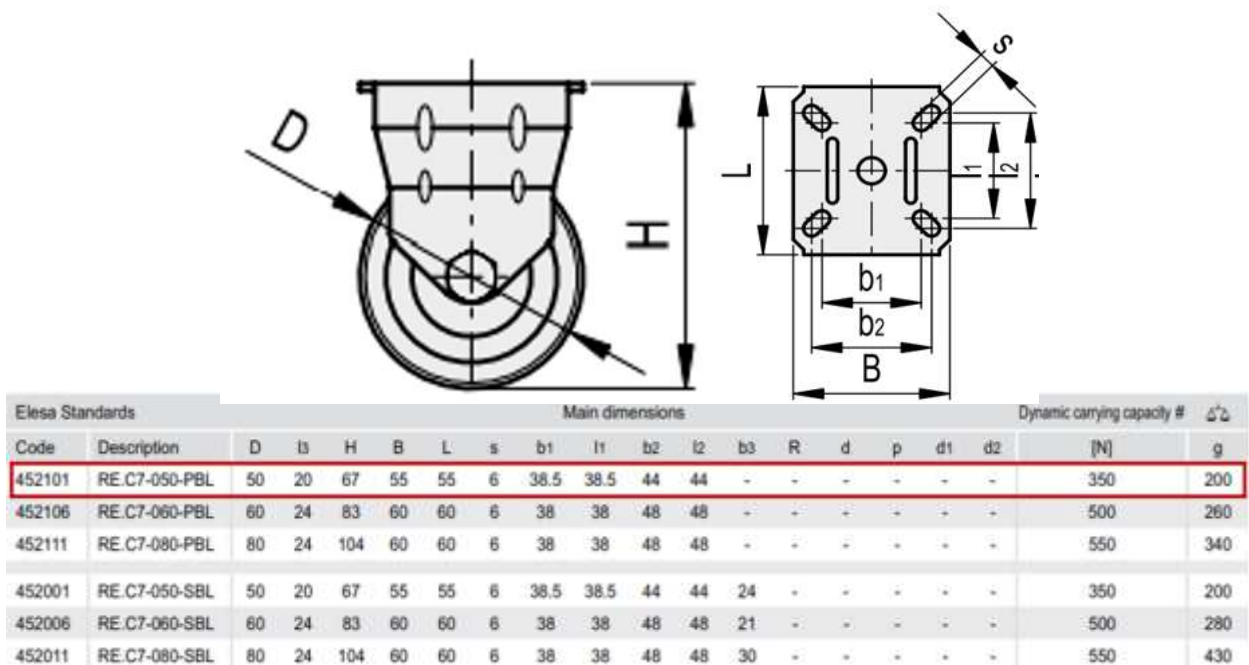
Dimensões da roda RE.C7-050-PBL. Adaptado de [17]
